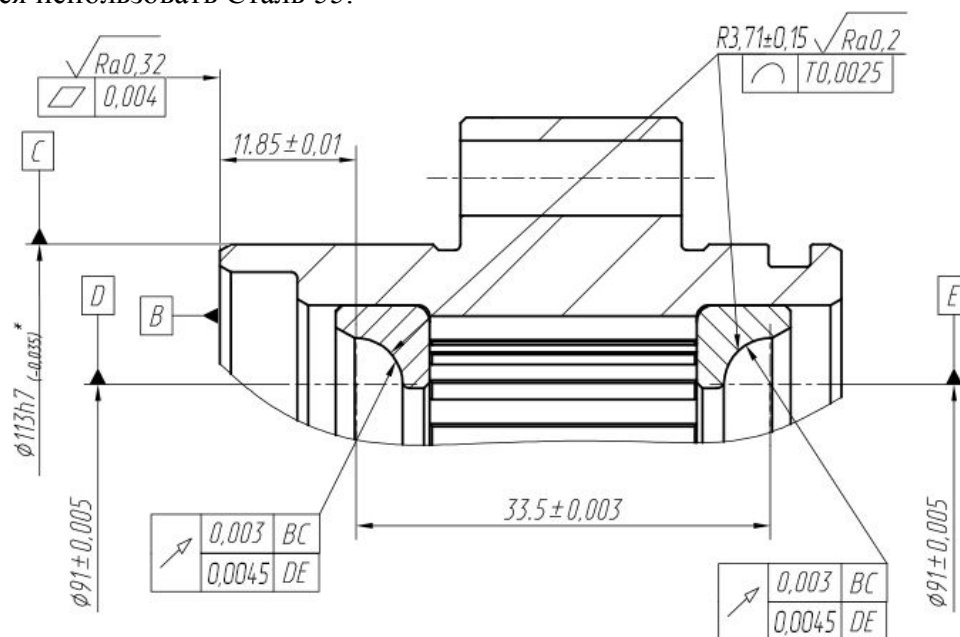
Фрагмент чертежа сборочной единицы «Корпус»
